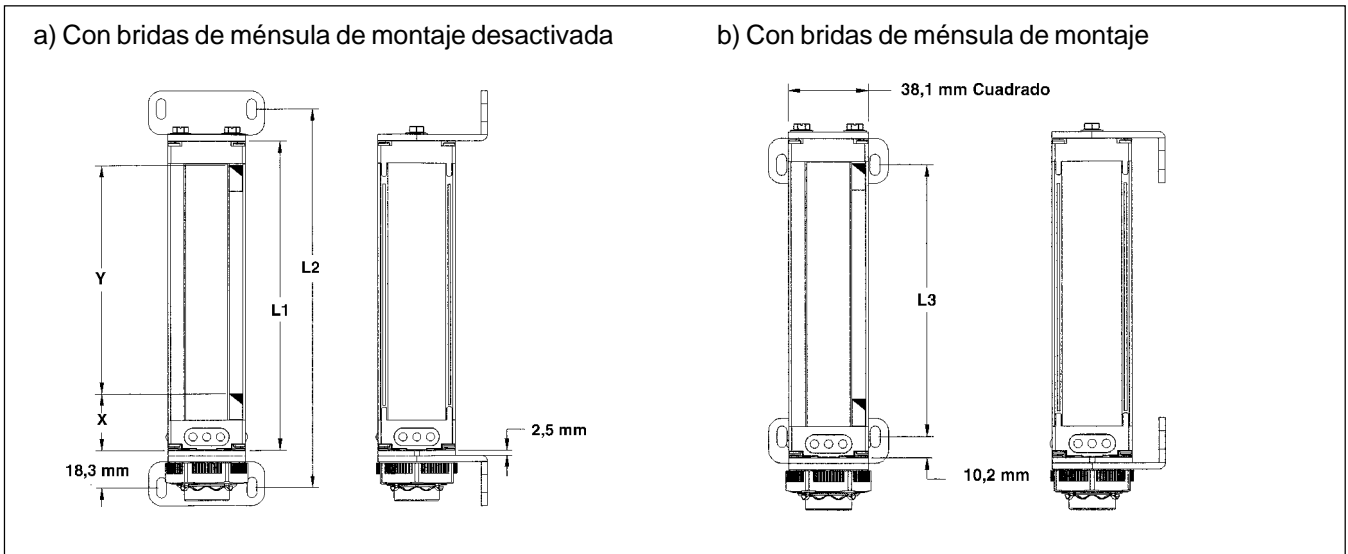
Dimensiones de Montaje de Emisor y Receptor y Localización del Área Definida
